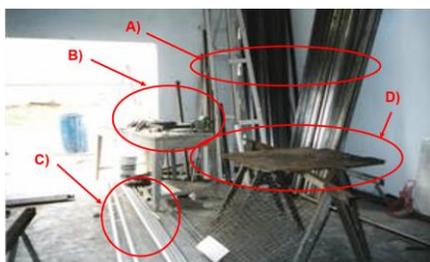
Ausencia de orden en el taller de soldadura y herrería.
